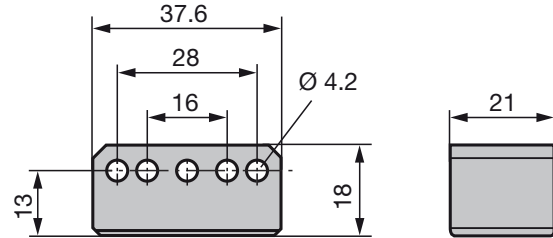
Dimensions de montage du capteur de position BTL6-A-3801-2
